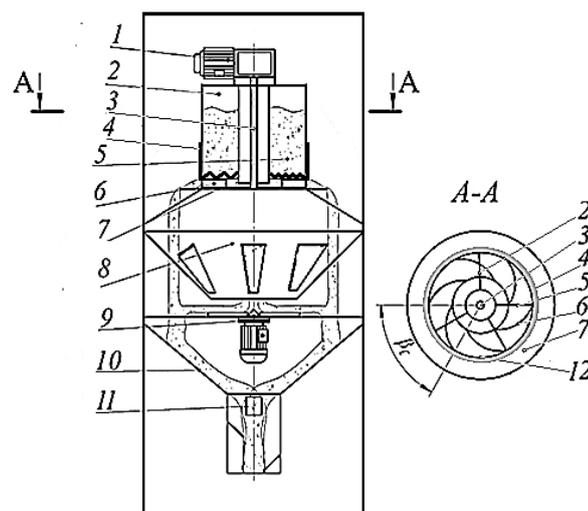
Конструктивно-технологическая схема дозационно-смесительного устройства: 1 — двигатель-редуктор; 2 — подвижная перегородка; 3 — передаточный вал; 4 — подвижная манжета; 5 — неподвижная промежуточная резка; 6 — лопата; 7 — диск; 8 — первая горловина; 9 — разбрасыватель со свободной передачей; 10 — второй горловина; 11 — доски; 12 — бункер
